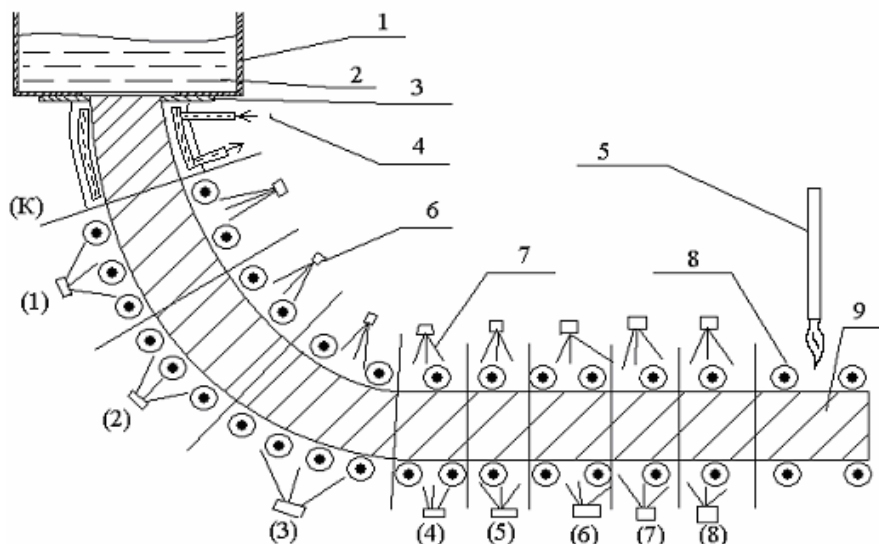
Схема МНЛЗ: 1 – пром. ковш; 2 – жидкая сталь; 3 – пластины формователи; 4 – нагнетатель воды в кристаллизаторе (К); 5 – система нарезки заготовок; 6 – форсунка подачи воды в зонах вод.-возд. охлаждения; 7 – охладитель (вода); 8 – прокатные валки; 9 – сляб
